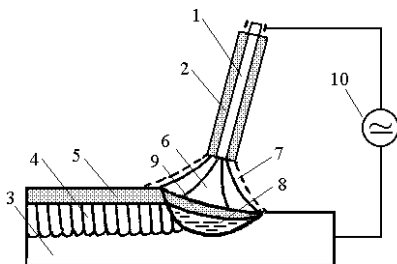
Схема ручной дуговой сварки плавящимся электродом с покрытием: 1 - стержень электрода; 2 - покрытие электрода; 3 - основной металл; 4 - сварной шов; 5 - твердая шлаковая корка; 6 - электрическая дуга; 7 - газовая защитная атмосфера; 8 - жидкая металлическая ванна; 9 - жидкая шлаковая ванна; 10 - источник тока
